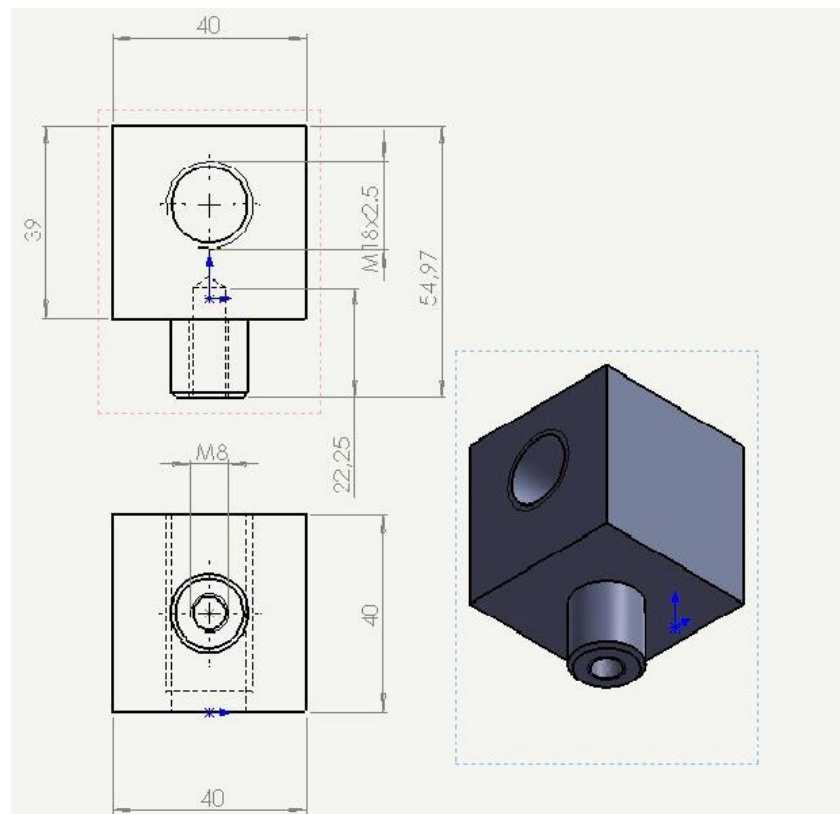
Dimensiones expresadas en milímetros y figura en 3D de la tuerca del tornillo sin fin del Eje Y
